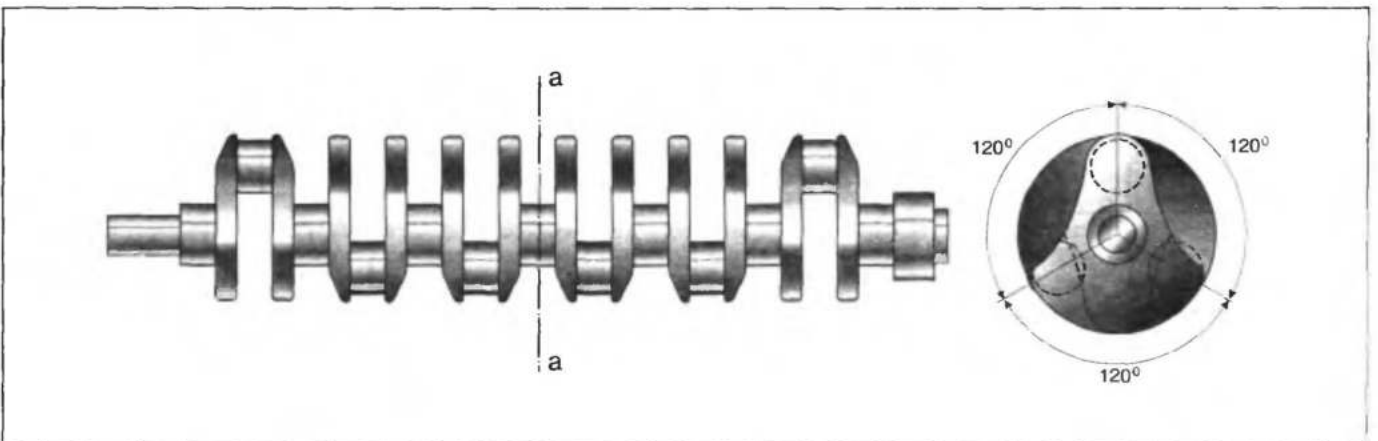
Семиопорный коленчатый вал рядного шестицилиндрового двигателя:
